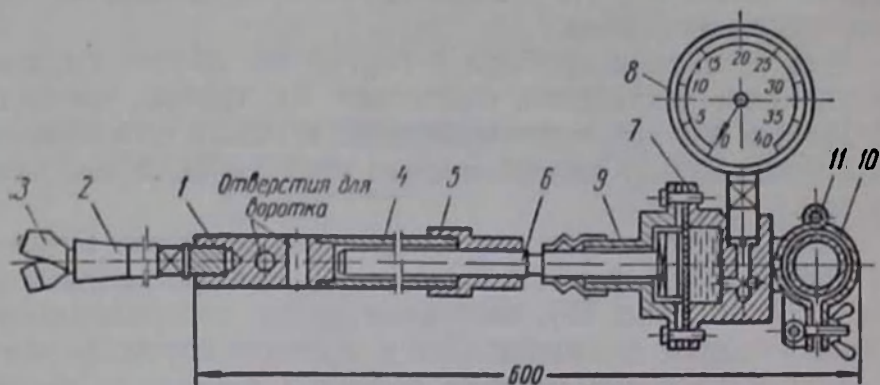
Схема прибора конструкции А. Н. Кульбачного:
